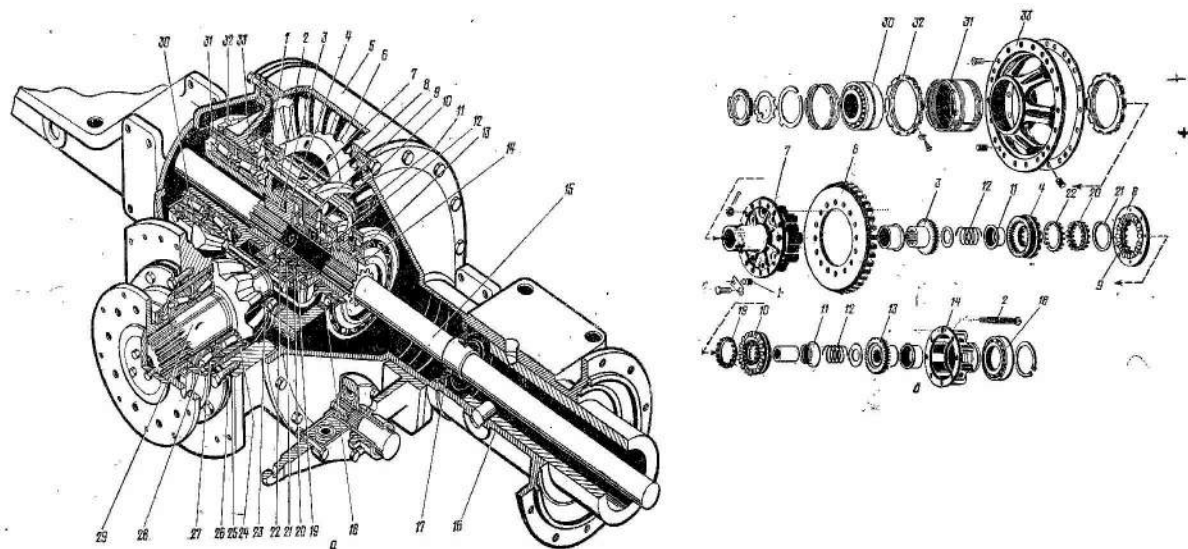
Главная передача ведущего моста: а—общий вид; б—детали; 1—штифт; 2—болт; 3 и 13—ступицы ведомых полумуфт; 4 и 10—ведомые полумуфты; 5—картер; 6—ведомая коническая шестерня; 7—ступица; 8—ведущая муфта; 9—шпонка; 11, 24 и 31—стаканы; 12—пружина; 14—чаша дифференциала; 15—полуось; 16—кожух полуоси; 17—крышка с уплотнением; 18—шарикоподшипник; 19 и 22—разрезные кольца; 20—кольцо ведущей муфты; 21—стопорное кольцо; 23—цилиндрический роликоподшипник; 25—регулирующие прокладки; 26—прокладки; 27 и 30—двухрядный конический роликоподшипник; 28—крышка; 29—ведущая коническая шестерня; 32—кольцевая гайка; 33—вставка.
